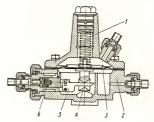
Регулятор расхода 1 — пружний; 2 — корпус; 3 — мембрана; 4 — тяга; 5 — рычаг; 6 — клапан собранный
